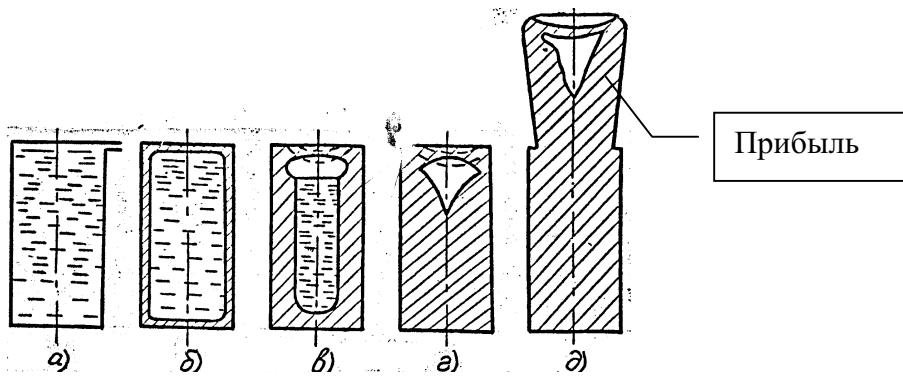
Образование усадочной раковины в отливке (а-д стадии процесса затвердевания).
